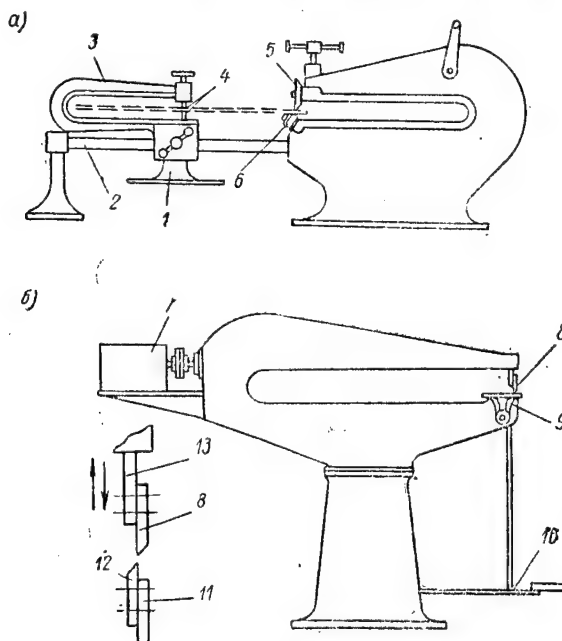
Машины для резки листового металла: а — дисковые ножницы; б — вибрационные ножницы.
